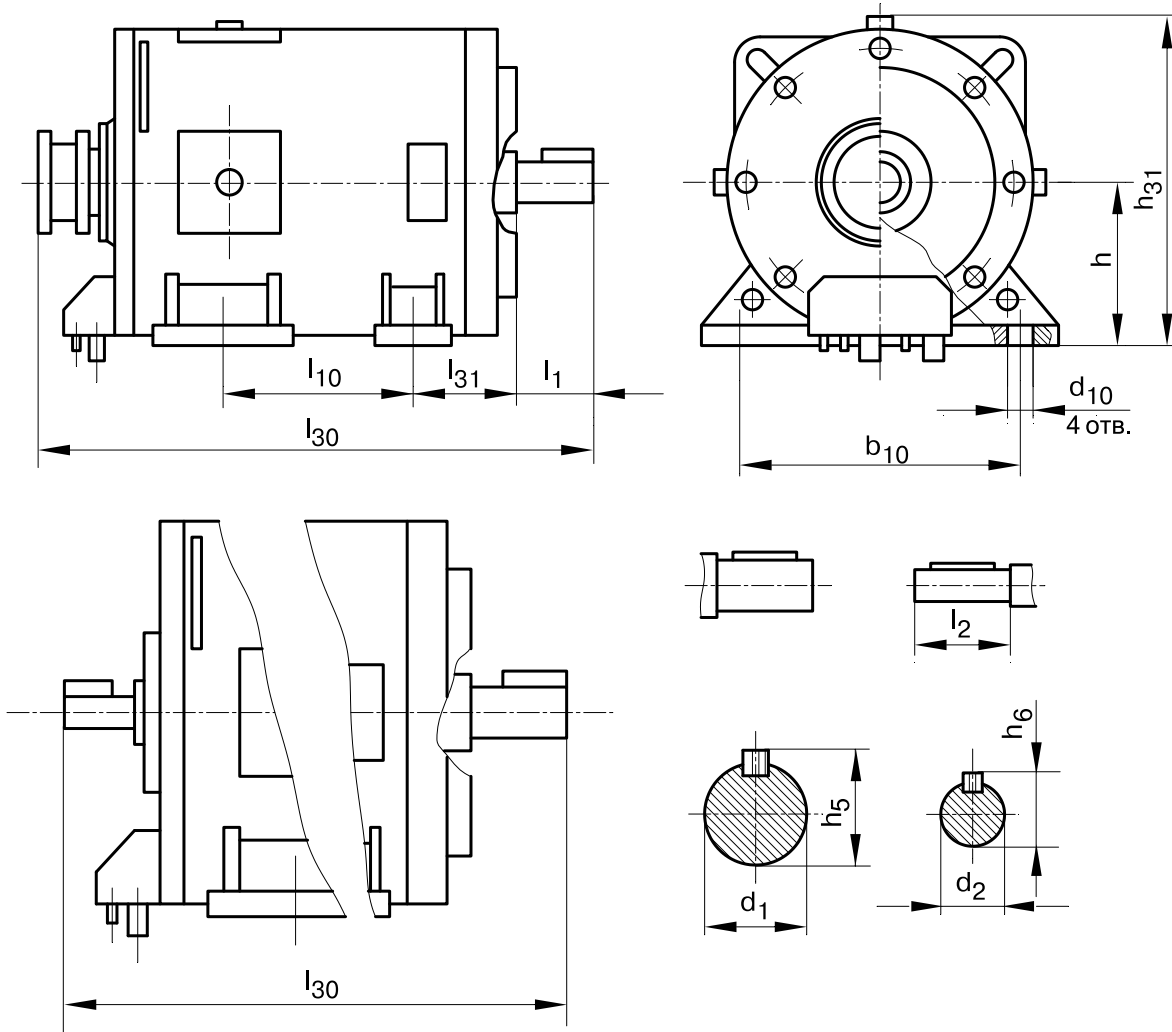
Габаритные, установочные и присоединительные размеры электрических машин типа ПП355, ПП400
